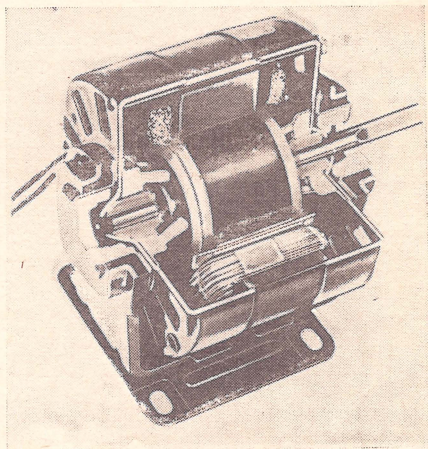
Двигатель с подачей дополнительной смазки к подшипнику
